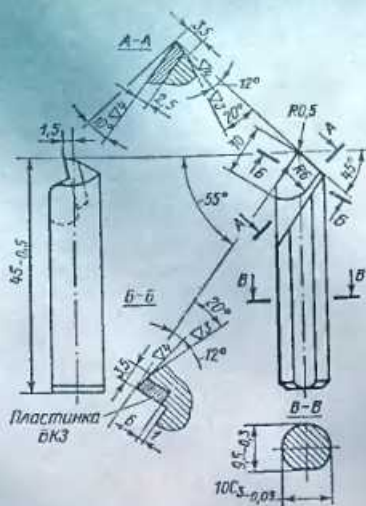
Резец для расточки втулок и вкладыша шатуна
